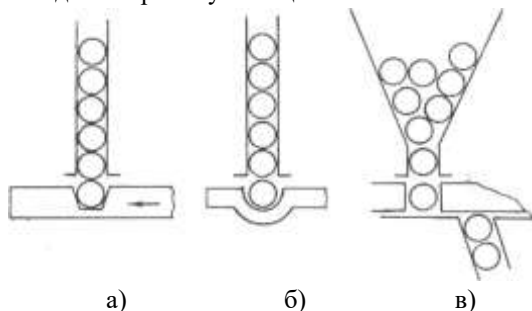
Способи подачі заготовок: а) – прямолінійний. б) – криволінійний. в) – бункерний.
